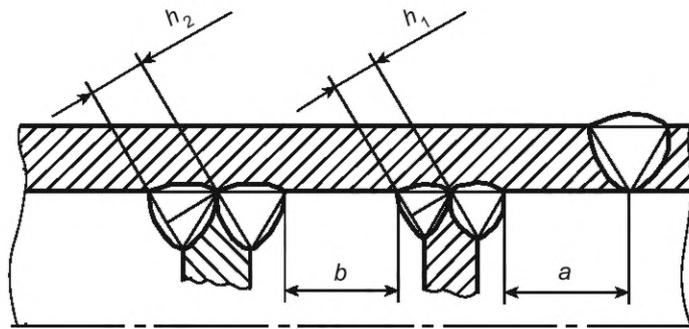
Расположение сварных соединений приварки деталей к оборудованию и трубопроводам
